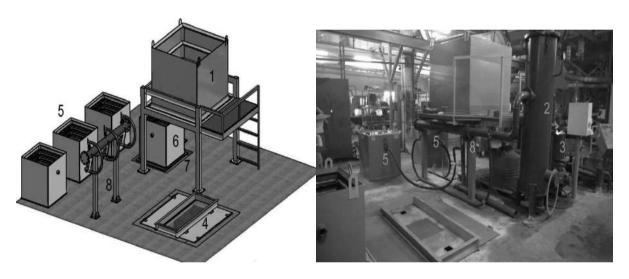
Формовочно-заливочный участок: а — схема; б — фотография; 1 — сменный раздаточный бункер; 2 — вакуумный аккумулятор; 3 — вакуумный водокольцевой насос; 4 — приямок; 5 — опоки под монорельсом заливочного ковша; 6 — опока на вибростоле; 7 — вибростол; 8 — стенд вакуумирования
